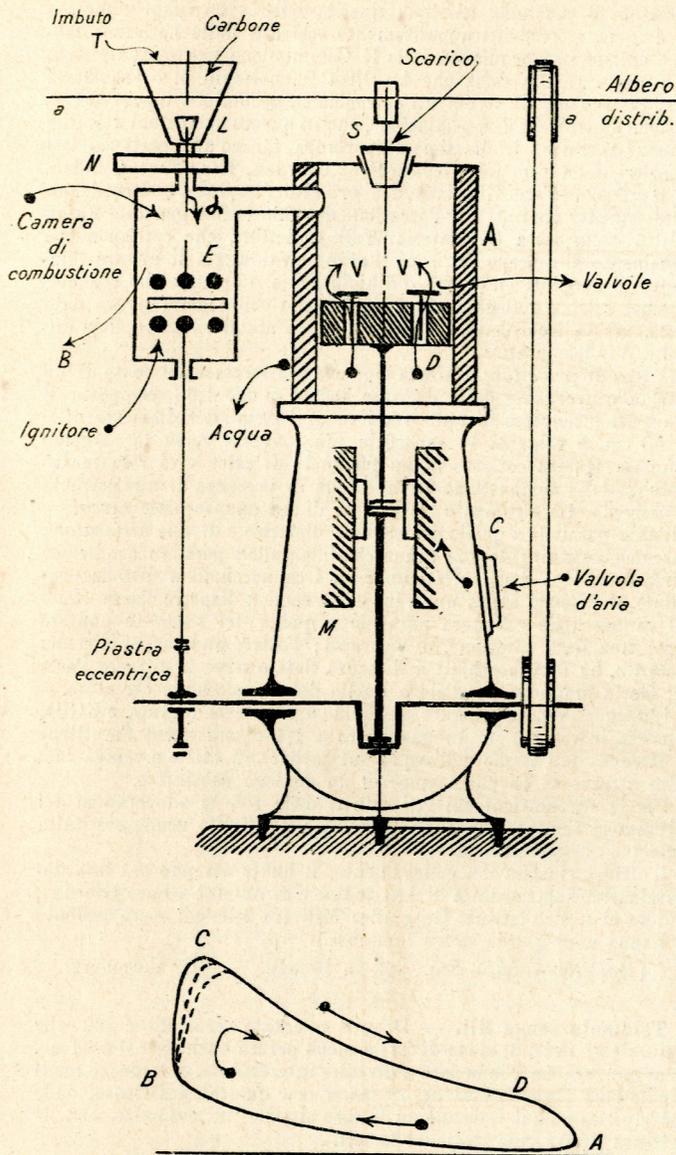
Schema del motore Maccalum a polvere di carbone.
